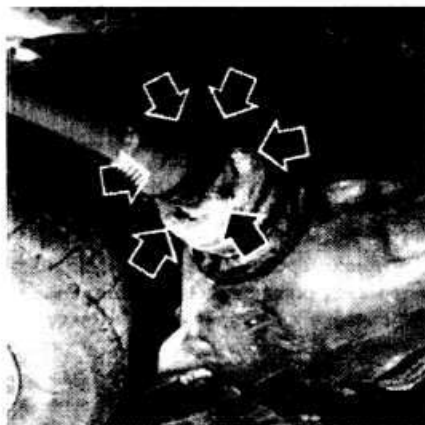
Стрелками показаны болты крепления вала привода колеса к фланцу выходного вала дифференциала
